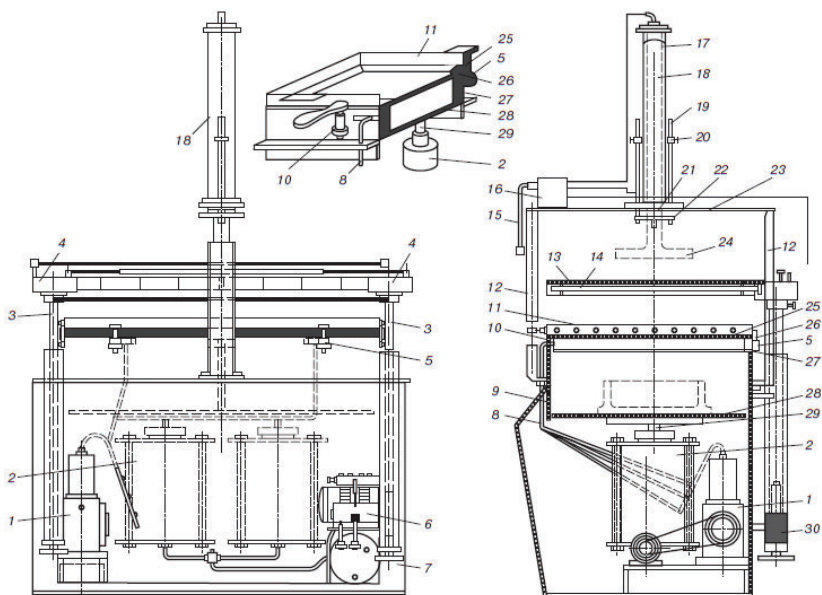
Схема однопозиційної машини з верхнім плунжером для попереднього механічного витягування
